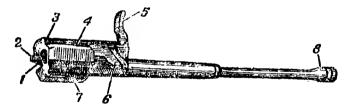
Затворияя рама с газовым поршиюм: I— канал для затвора; 2— предохранительный выступ; 3— выступ для опускания рычага автоспуска; 4— паз для отгиба ствольной коробки; 5— рукоятка; 6— фигурный вырез; 7— паз для отражательного выступа; 8— газовый поршень
